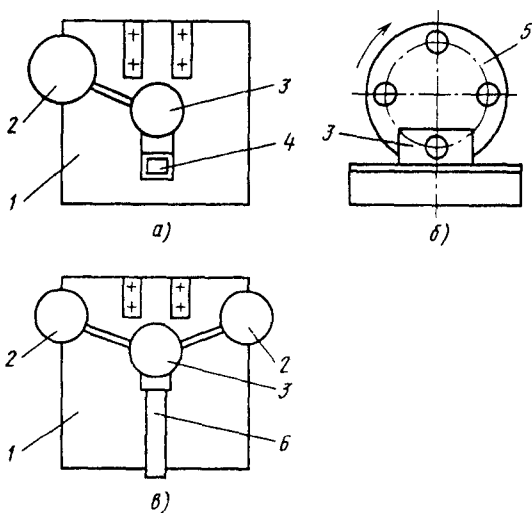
Схема однопозиционных сборочных полуавтоматов (а, б) и автоматов (в): 1 — стол; 2 — вибробункер, 3 — сборочная головка, 4 — базирующее устройство; 5 — поворотный стол; 6 — лоток
